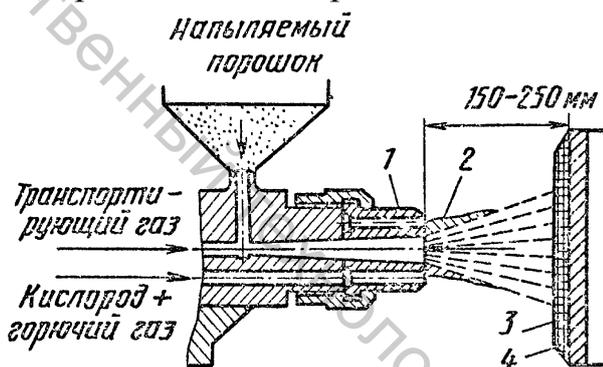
Схема газопламенного напыления порошкового материала с помощью транспортирующего газа:
